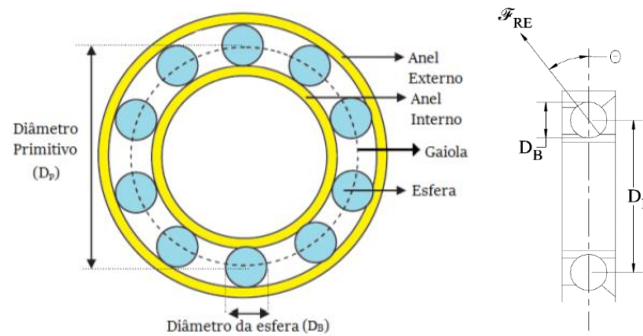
Constituição e dimensões de um rolamento [8-12].
